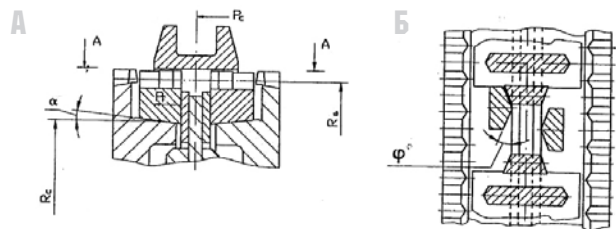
Расчетная схема угла блокировки синхронизатора основного редуктора
